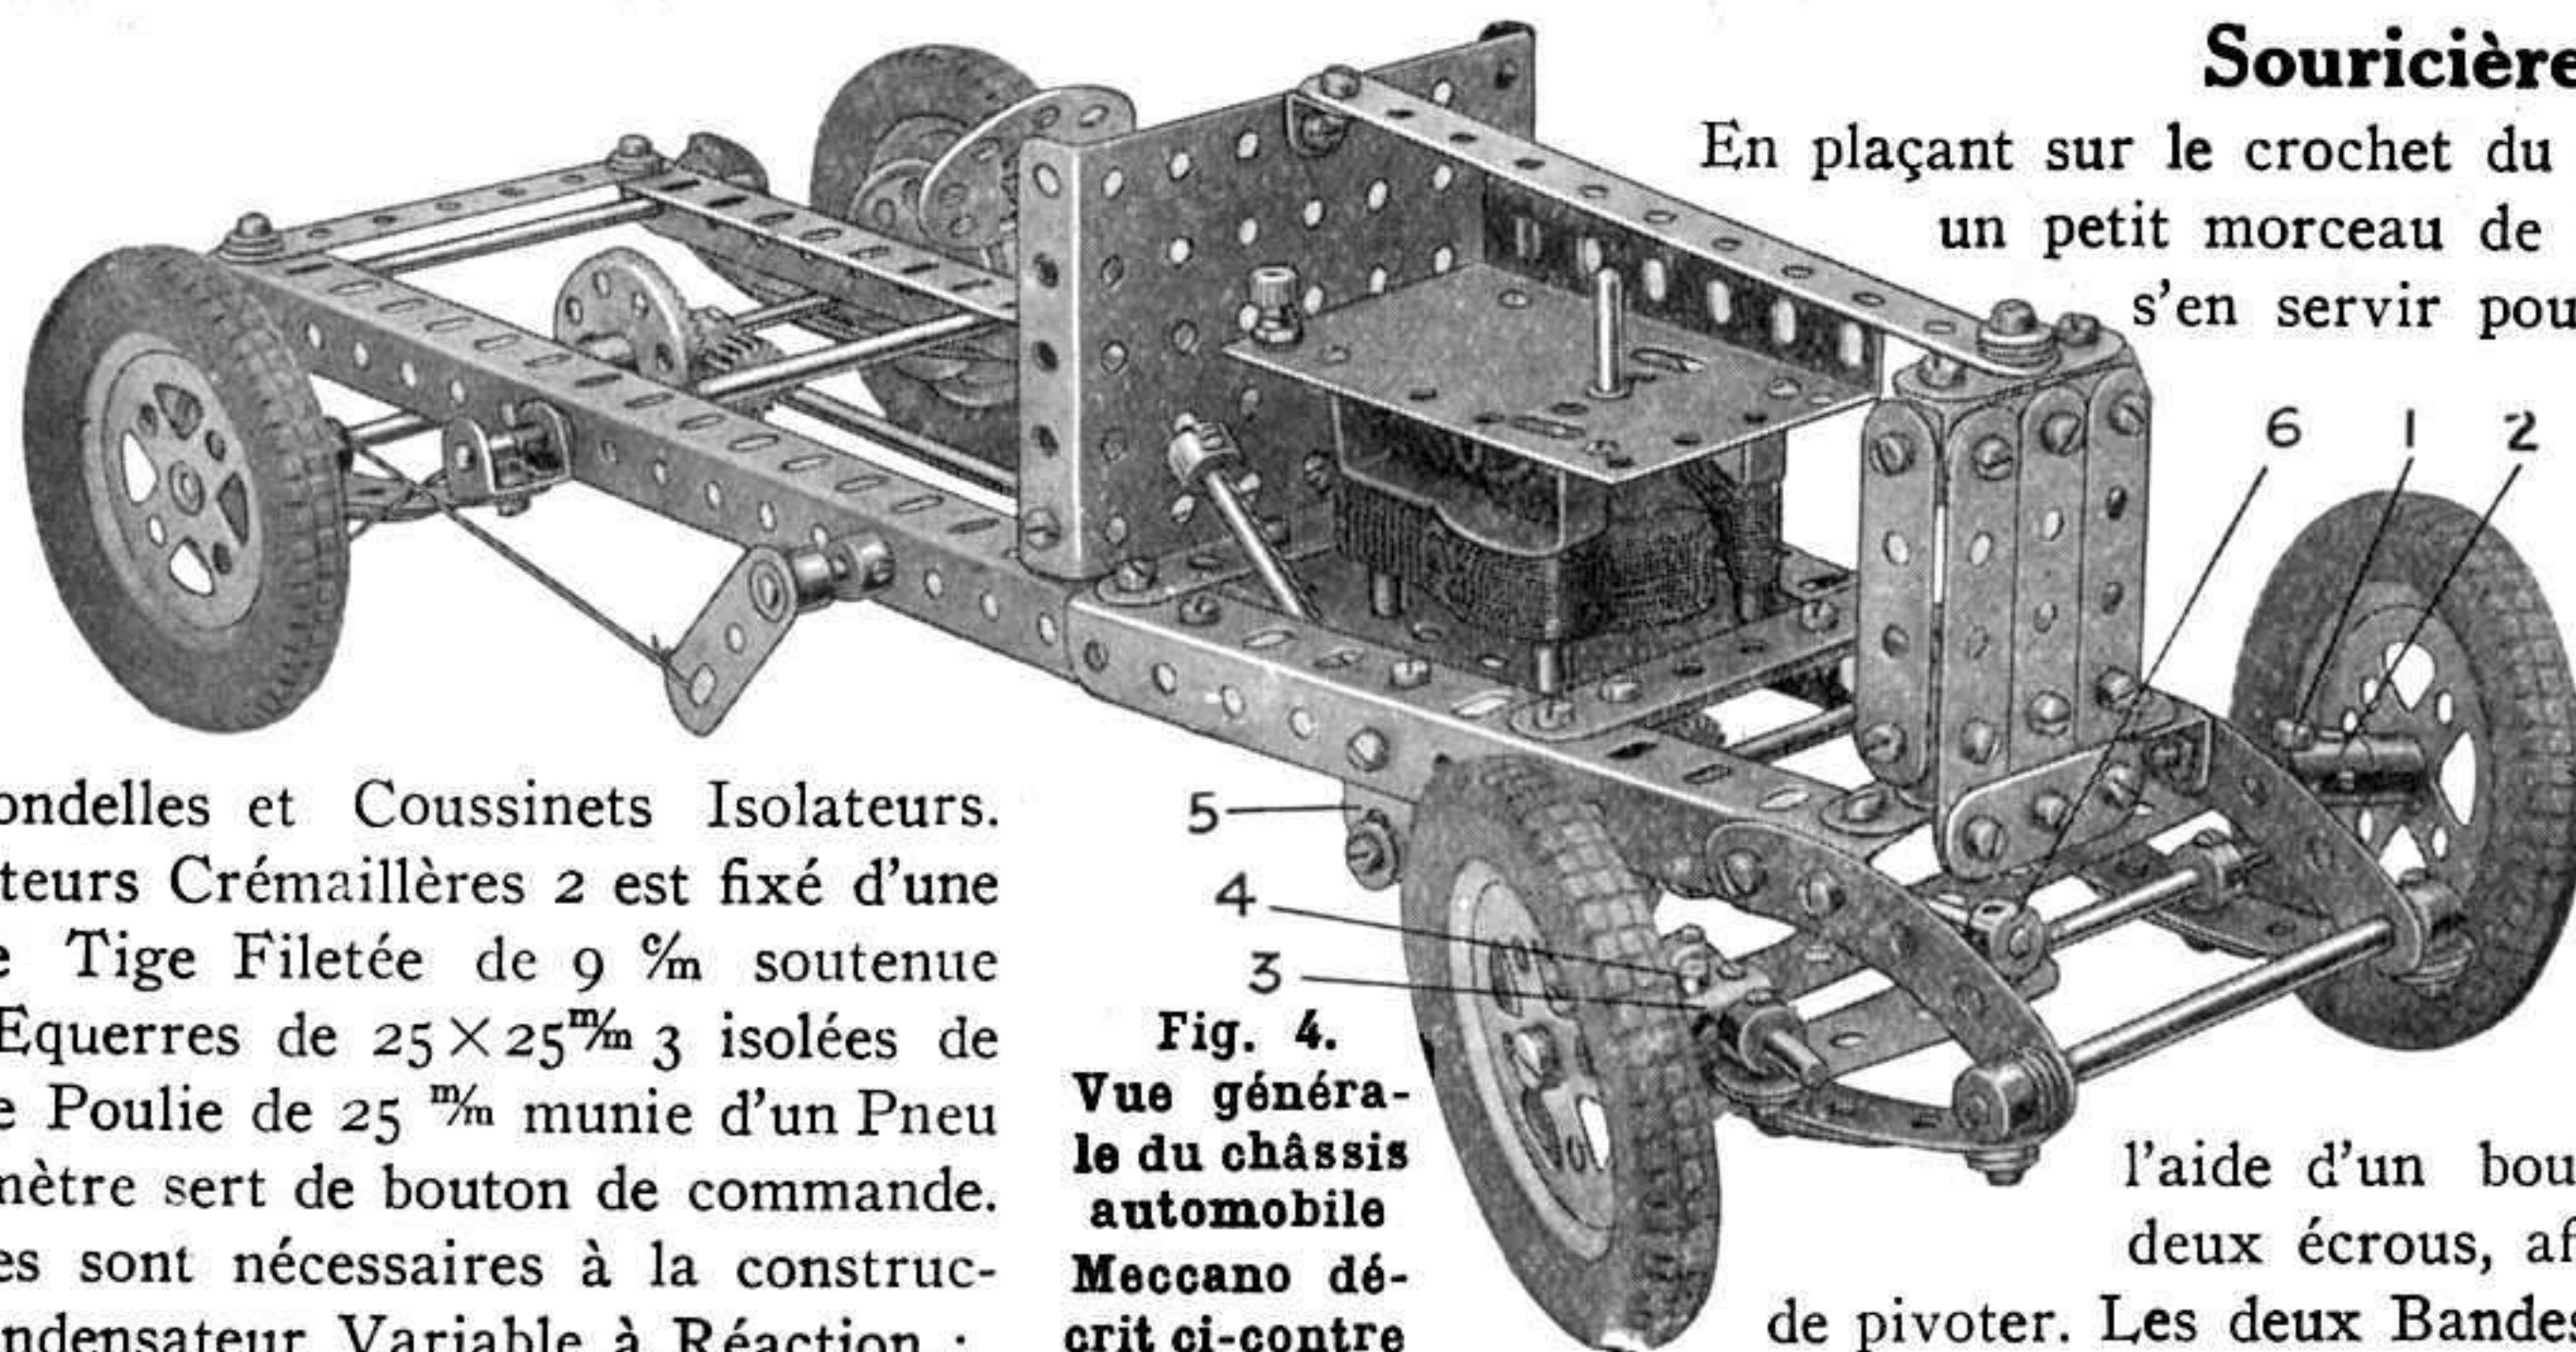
Vue générale du châssis automobile Meccano décrit ci-contre
